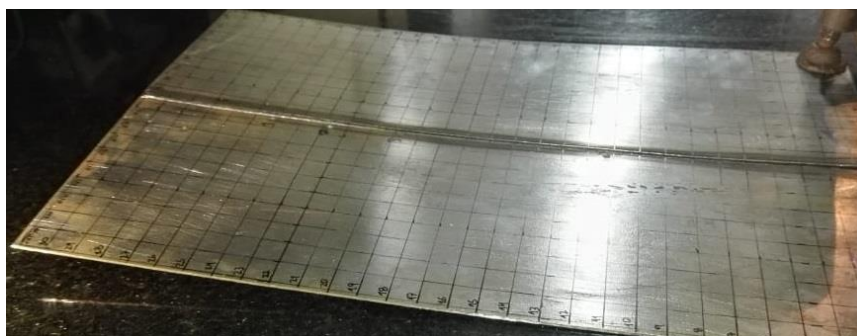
16 – Imagem final da chapa soldada pelo processo TIG.
